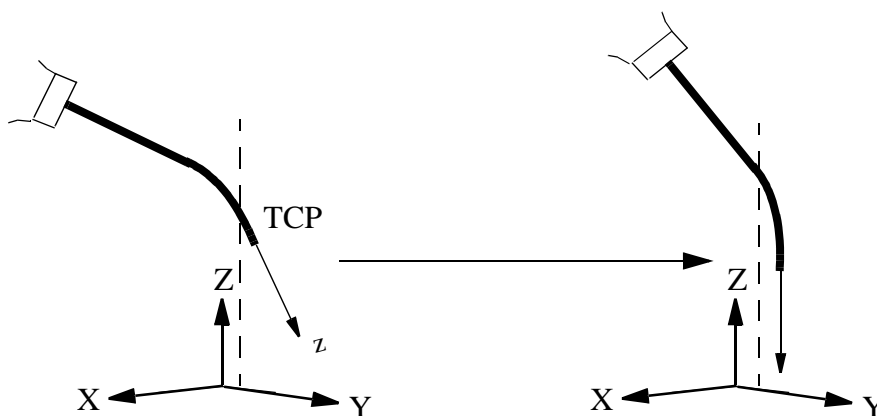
Das Werkzeug wird mit der Z-Achse ausgerichtet.
